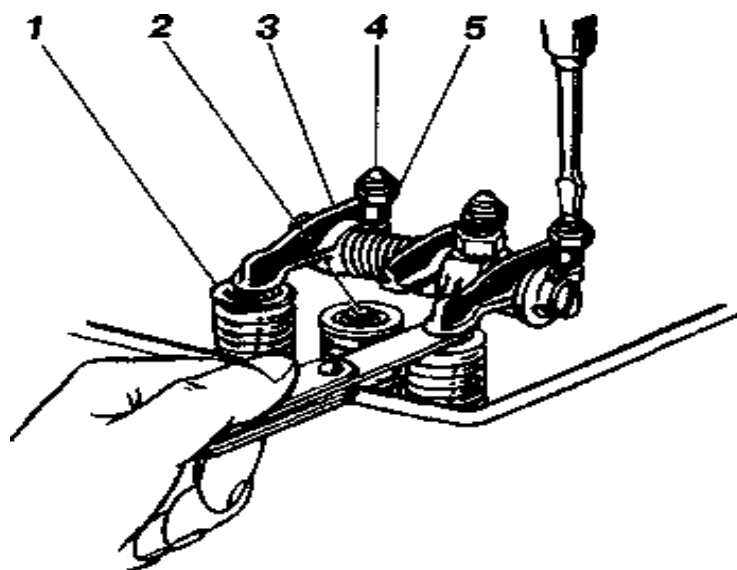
Порядок установки зазору між носком коромисла і торцем стержня клапана в разі нижнього розташування розподільного вала
